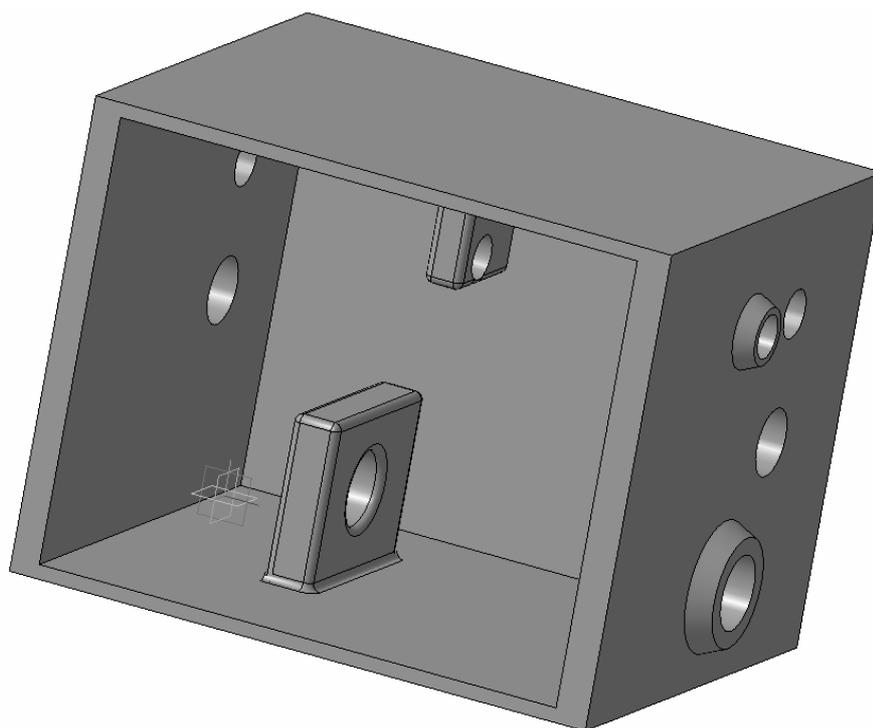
Модель корпуса коробки с необходимыми отверстиями
